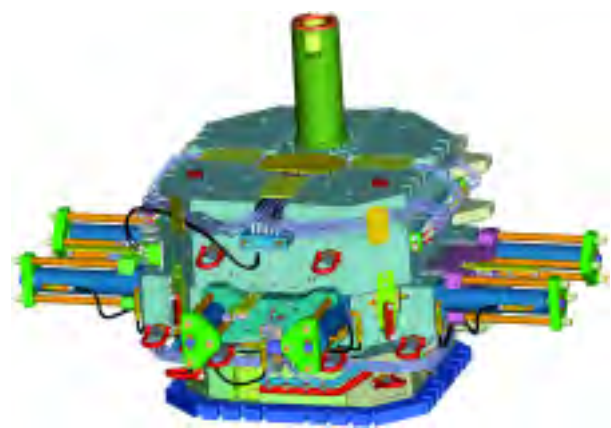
Imagen del molde completo cerrado para un bloque motor de 4 cilindros.
